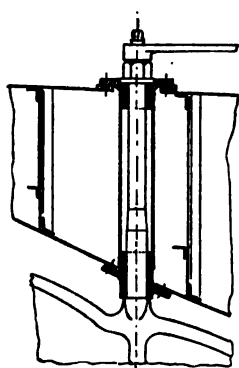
Aufgehängtes, eisernes Schweberuder.
